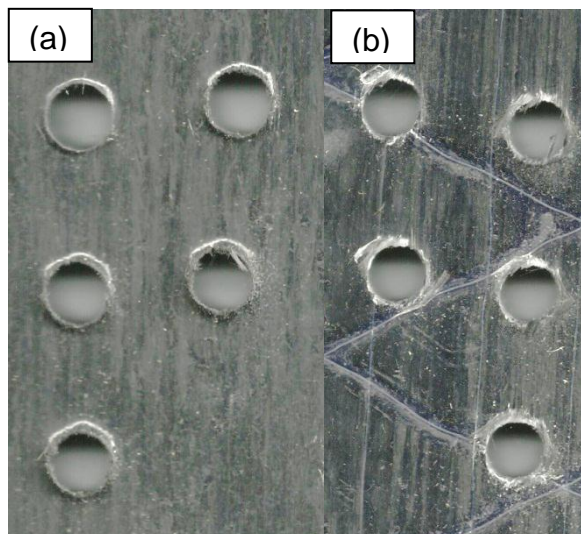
Furações realizadas com a broca para madeira: (a) Superfície de entrada; (b) Superfície de saída.
